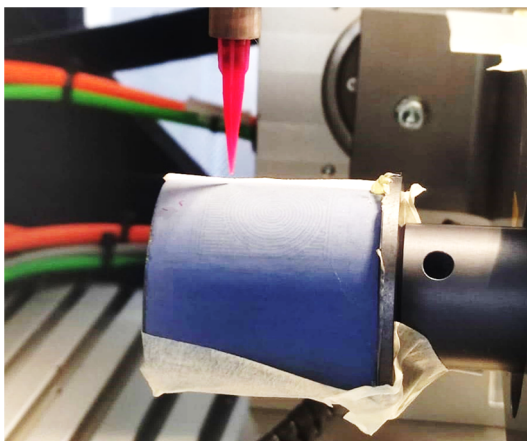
Proceso de impresión de material conductor sobre Tubacoat.
